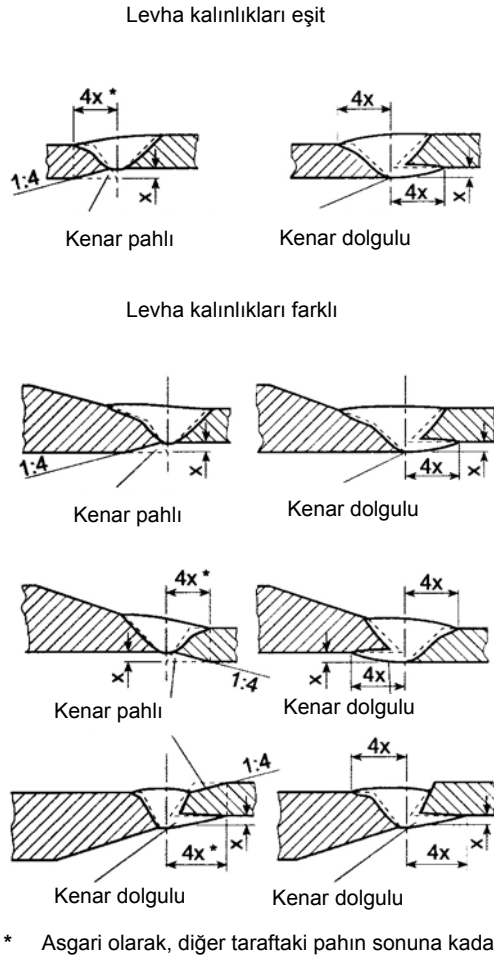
Farklı boyutlardaki bileşenler arasındaki geçişler
